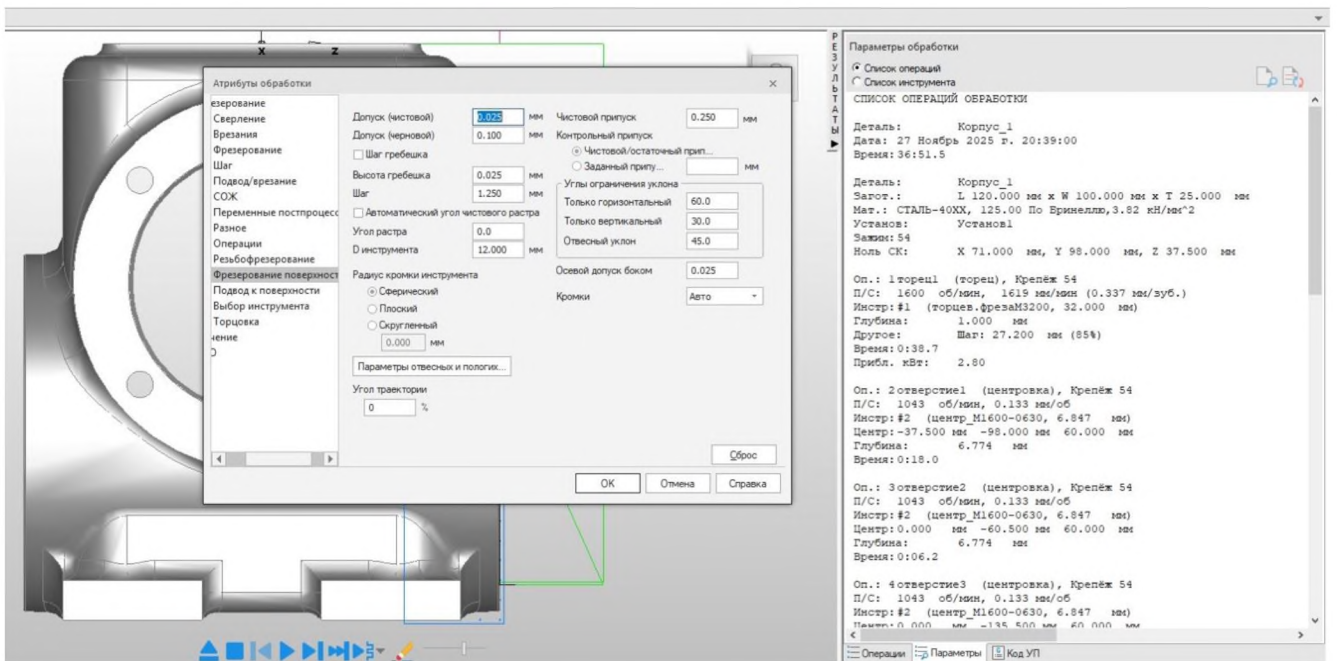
Введення атрибутів обробки деталі «Корпус»
